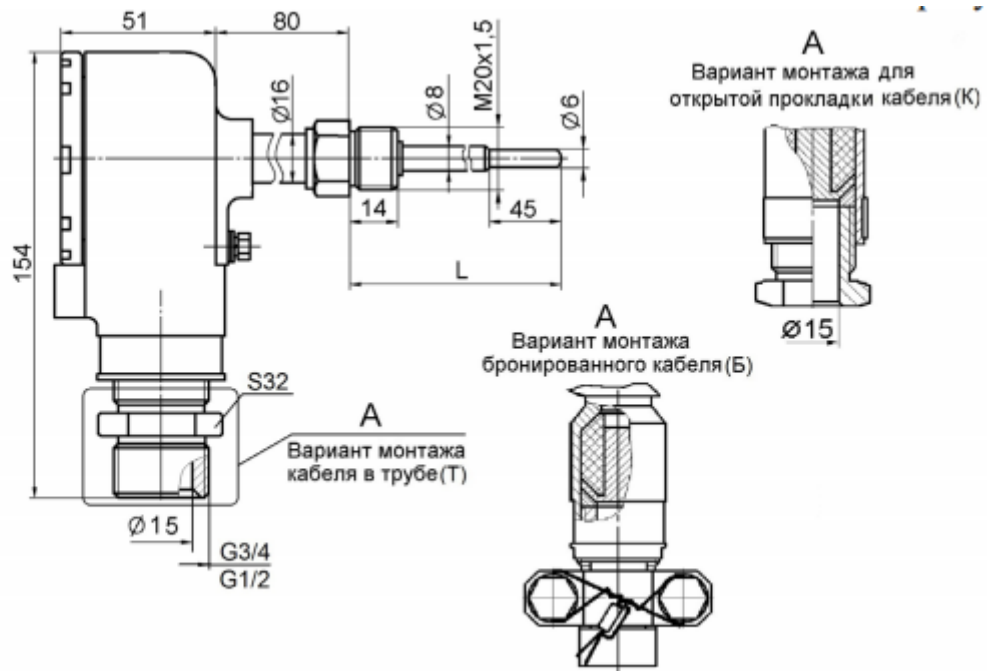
Головка из алюминиевого сплава. Штуцер неподвижный
